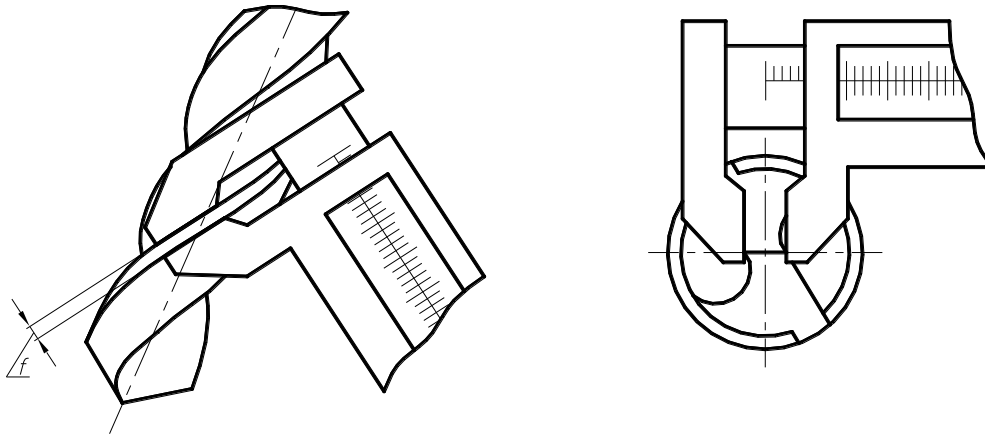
Измерение длины поперечной кромки и ширины ленточки сверла штангенциркулем
